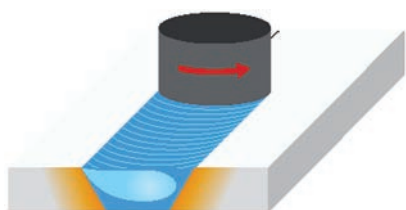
Схематическое изображение ротационной сварки трением перемешиванием (СТП)
